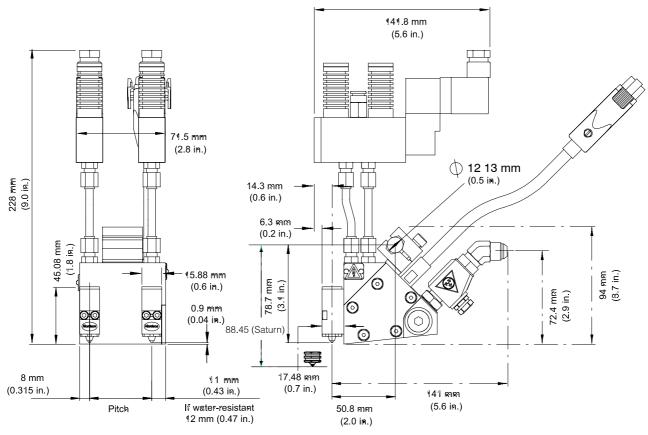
Dimensioni di una pistola configurabile multimodulo con elettrovalvola SG
